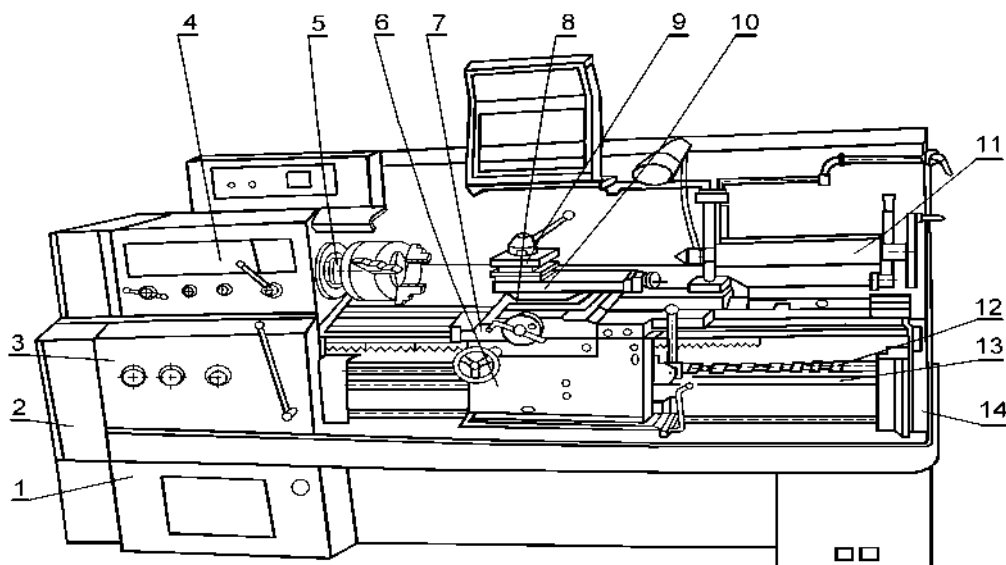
Конструкція токарно-гвинторізного верстата мод.16К20
